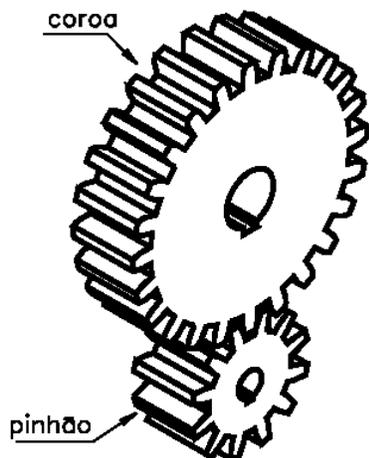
Engrenagem cilíndrica de dentes retos
